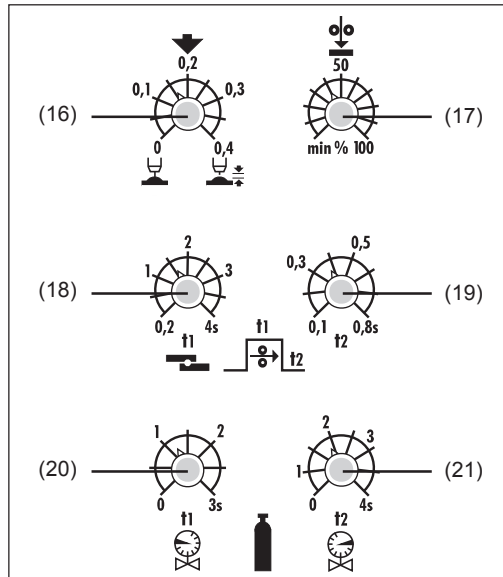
Os vários controlos de definição da parte interior do aparelho de soldadura
